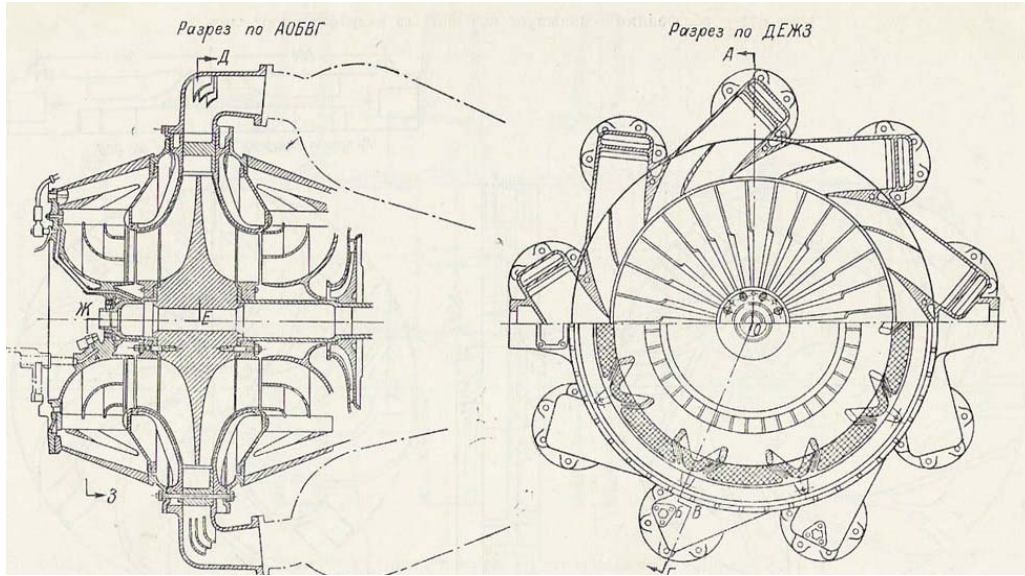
Центробежный компрессор турбореактивного двигателя с двухсторонним входом
